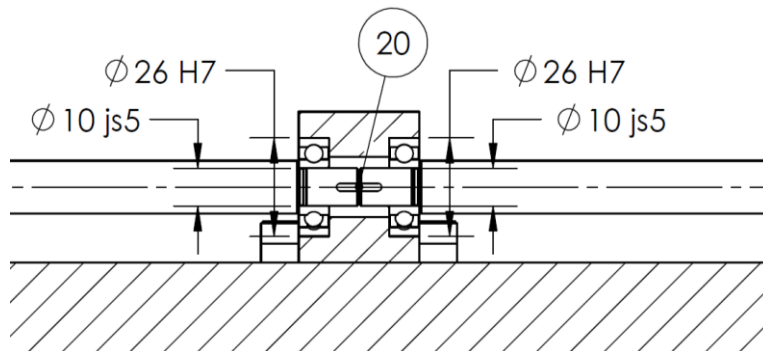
Vista en corte Caja de Rodamientos 2 [Elaboración Propia]
